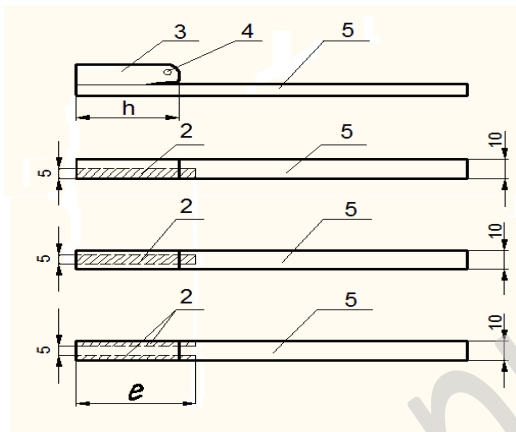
Образцы муфтового сварного соединения ПЭ труб для испытания на отслаивание с различными положениями сваренной области на испытываемом образце (нагревательная спираль не приведена)
